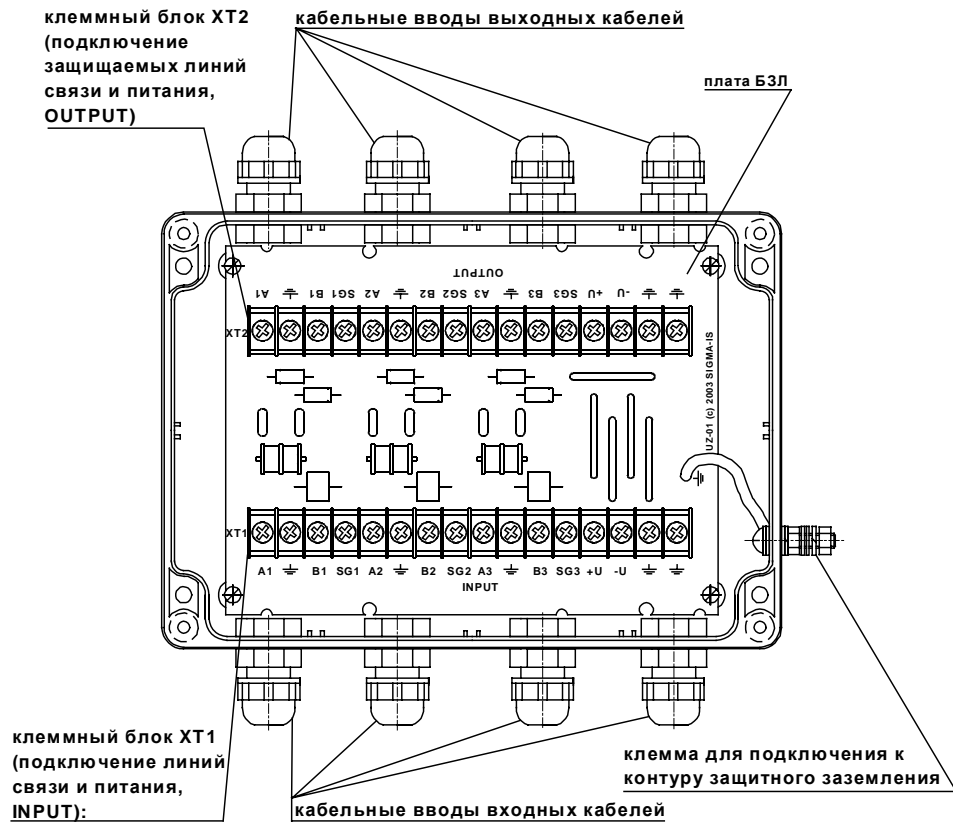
БЗЛ-01, БЗЛ-04 (вид без крышки корпуса)
